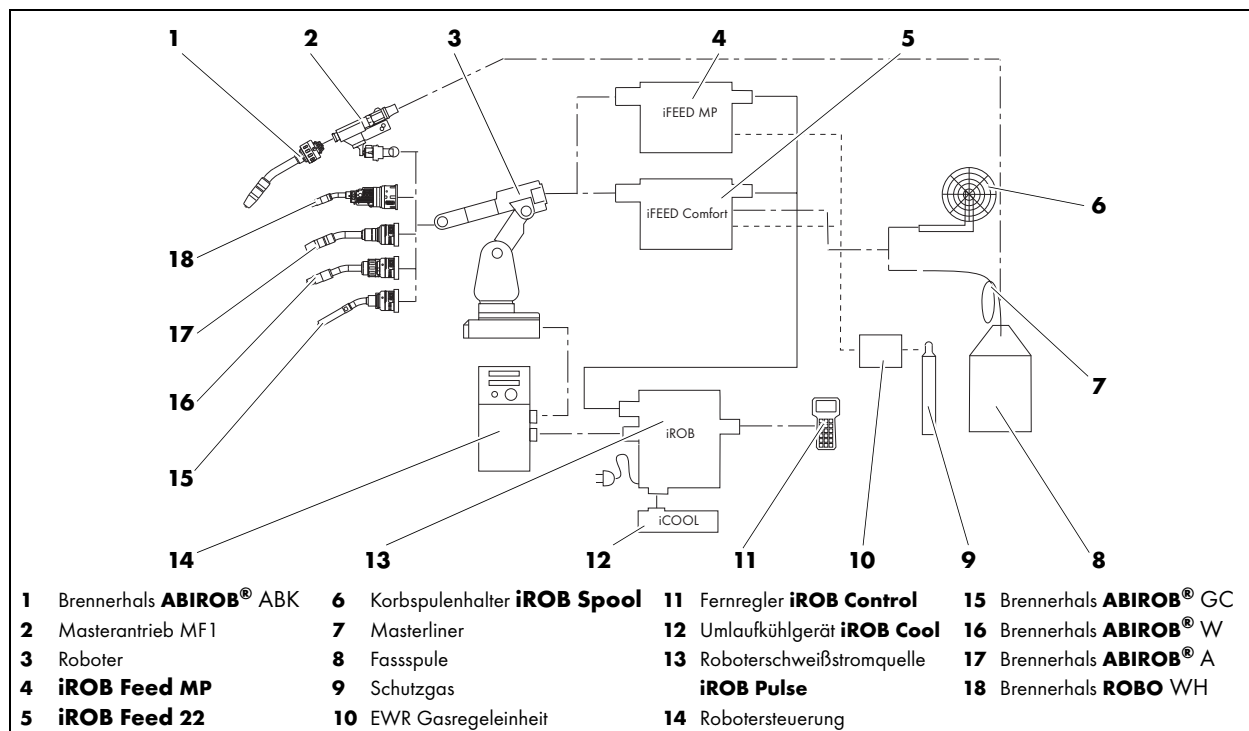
Komponenten Roboterschweißausrüstung
